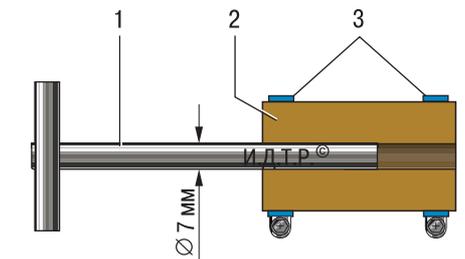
Приспособление для притирки клапанов: 1 – металлический стержень; 2 – резиновый шланг; 3 – винтовые хомуты
